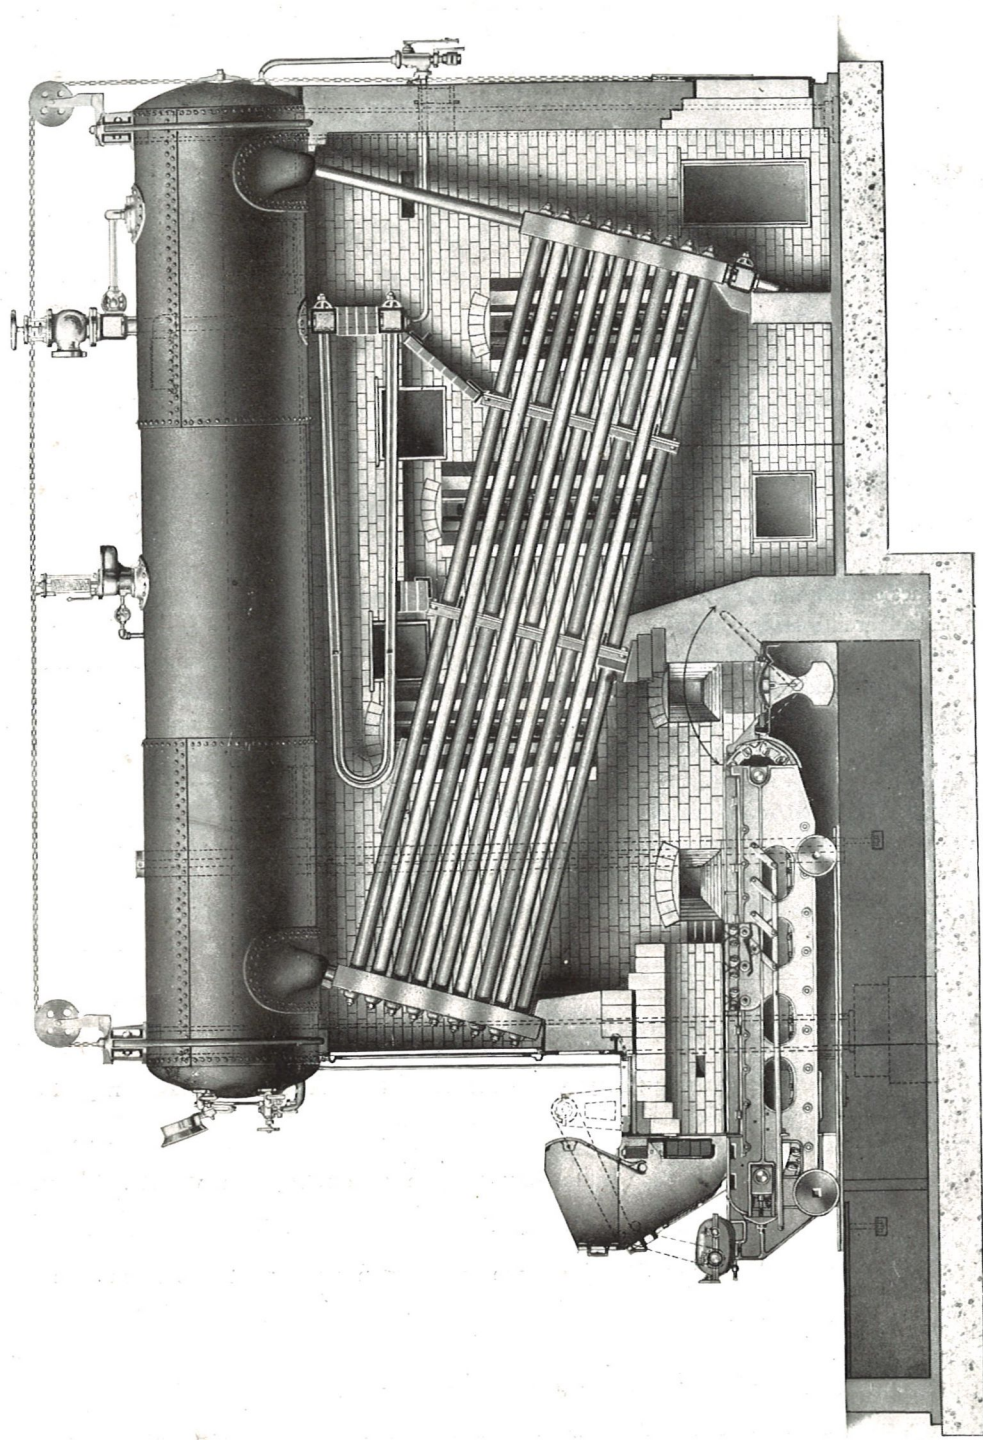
ENSEMBLE D'UNE CHAUDIERE BABCOCK & WILCOX,
